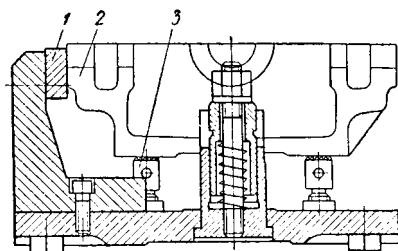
Фрезерное приспособление с установкой заготовки по разметке
